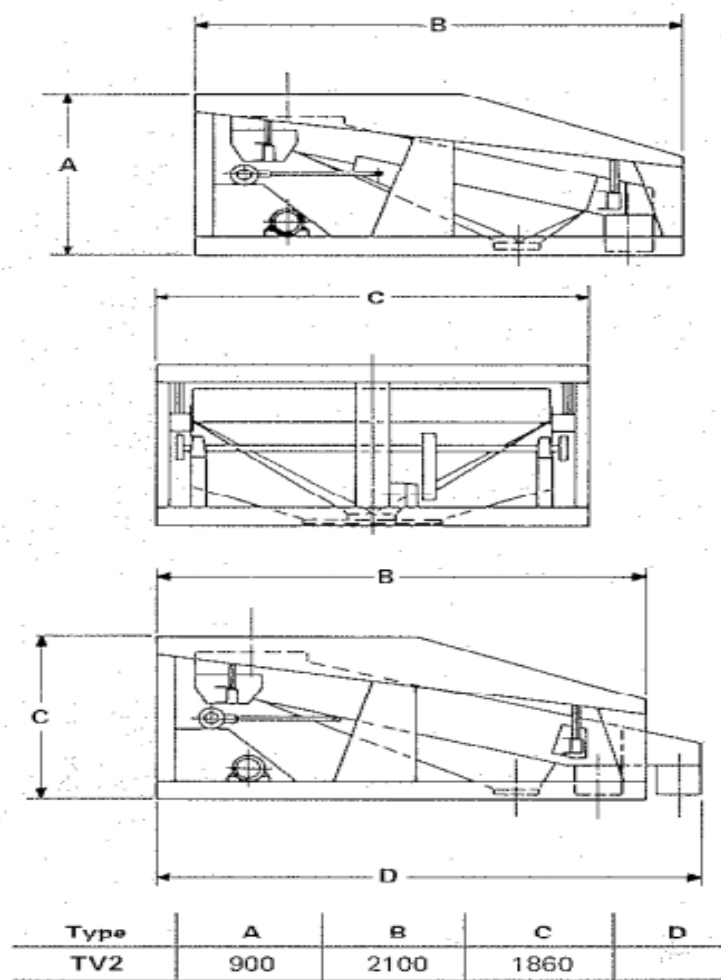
Dimensiones del tamizador. Fuente: Promill-Stolz.
